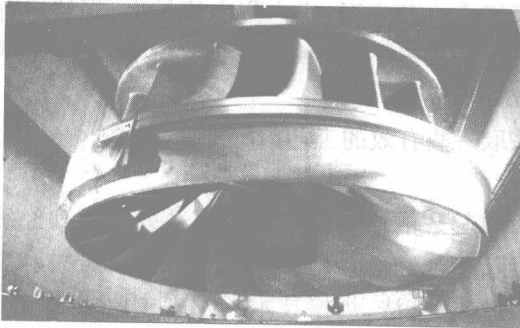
三峡不锈钢水轮机焊接转轮
